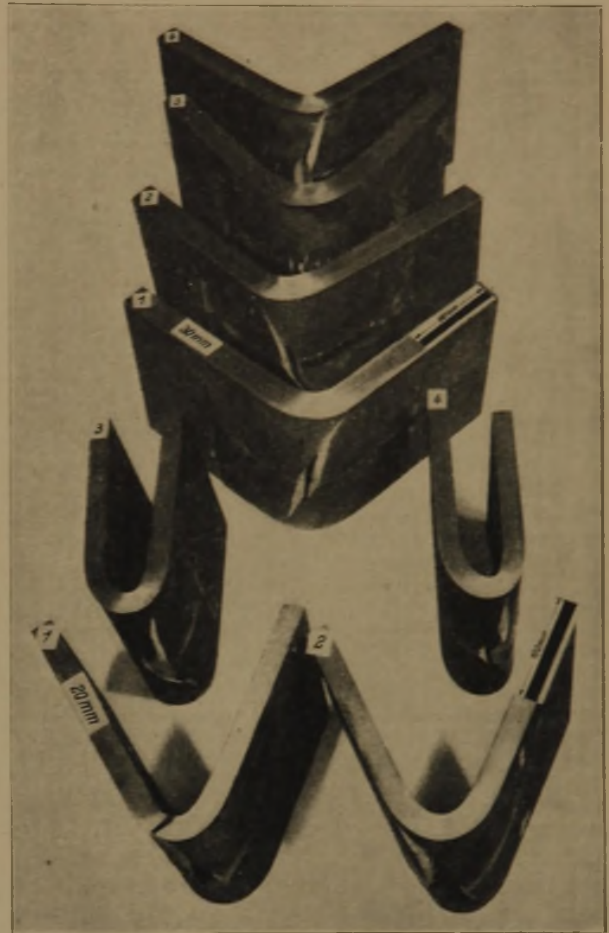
Aufschweißbiegeproben von 20 und 30 mm dicken normalgeglühten Blechen des Gusses 28 438.
